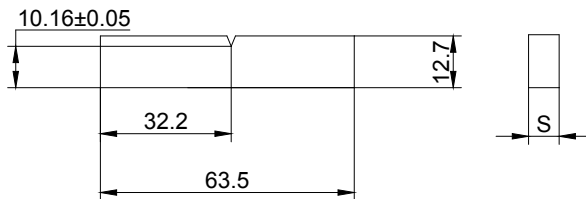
Probeta para ensayo de impacto IZOD.
